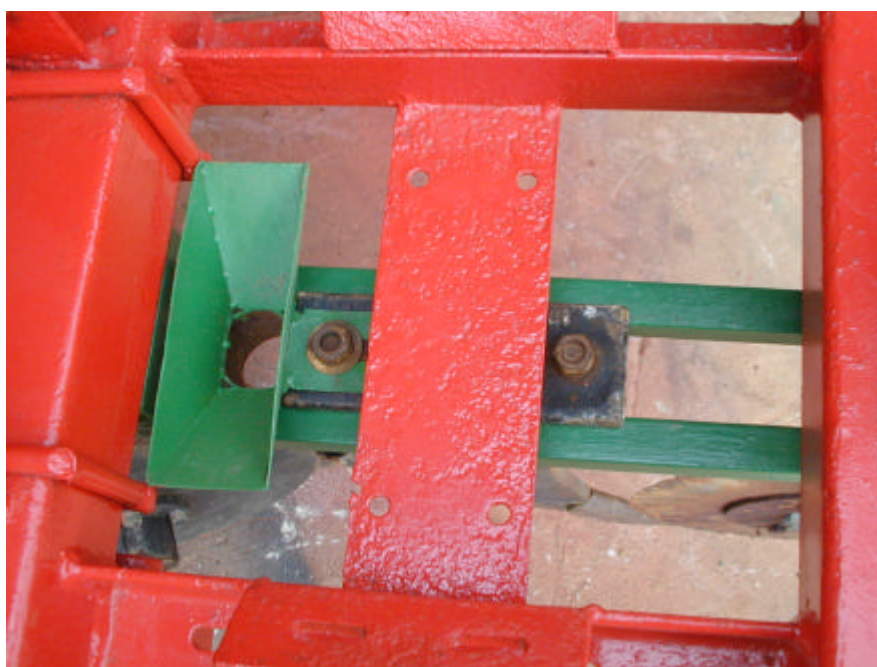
D – Vista superior do suporte do sulcador e parte do mecanismo coletor de adubo.
